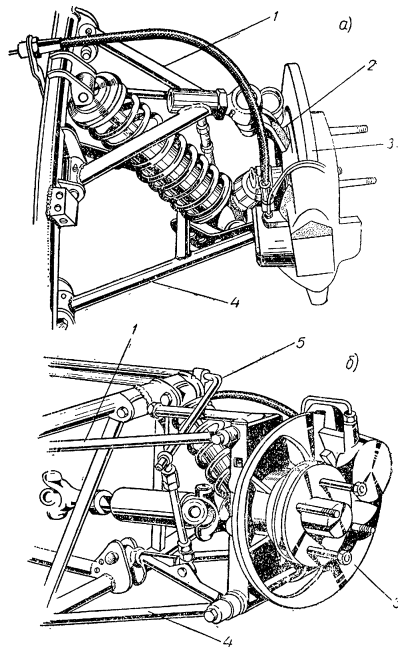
Подвеска автомобиля «Скараб»: а — подвеска передних колес; б — подвеска задних колес; 1 — верхний рычаг подвески; 2 — поворотная стойка; 3 — дисковый тормоз; 4 — нижний рычаг; 5 — торсионный стабилизатор
